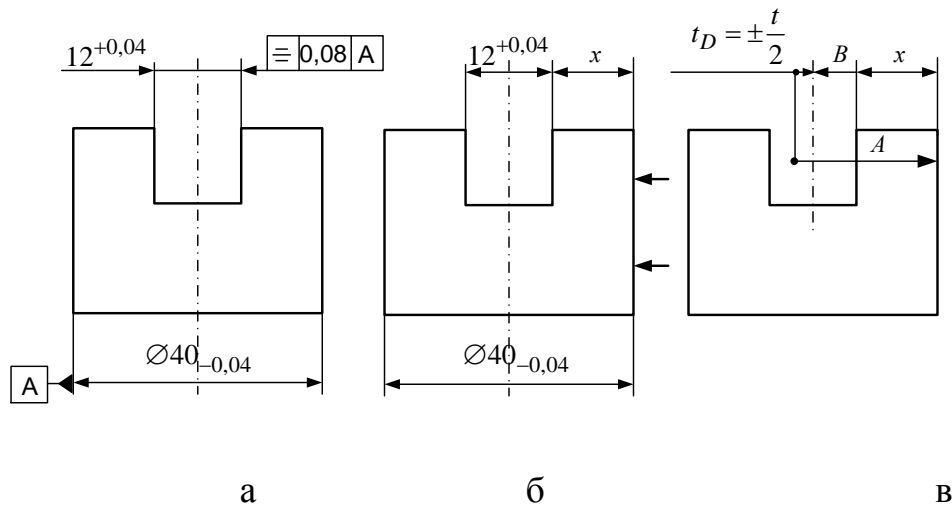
Размерная цепь, включающая допуски размеров и допуски симметричности: а – чертеж детали; б – эскиз обработки; в – размерная цепь для расчета размера x для контроля
